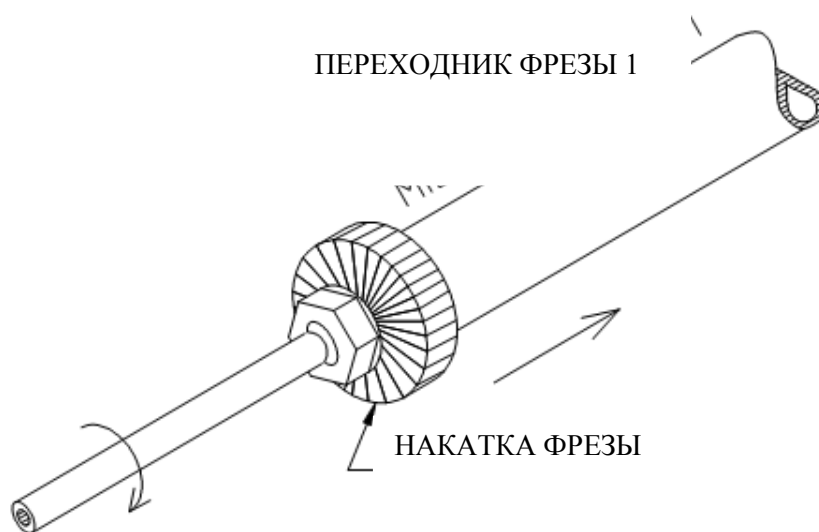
Обработка посадочных поверхностей приварных деталей.
